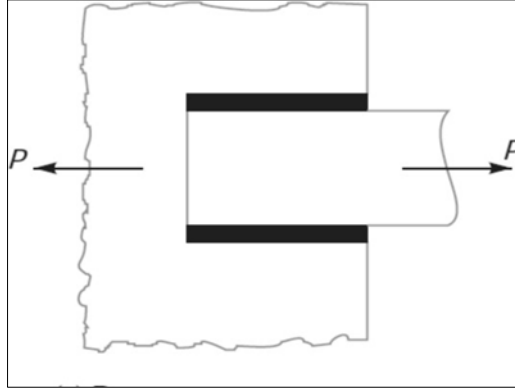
पॅरालेल फिलेट वेल्ड (Double parallel fillet weld)
